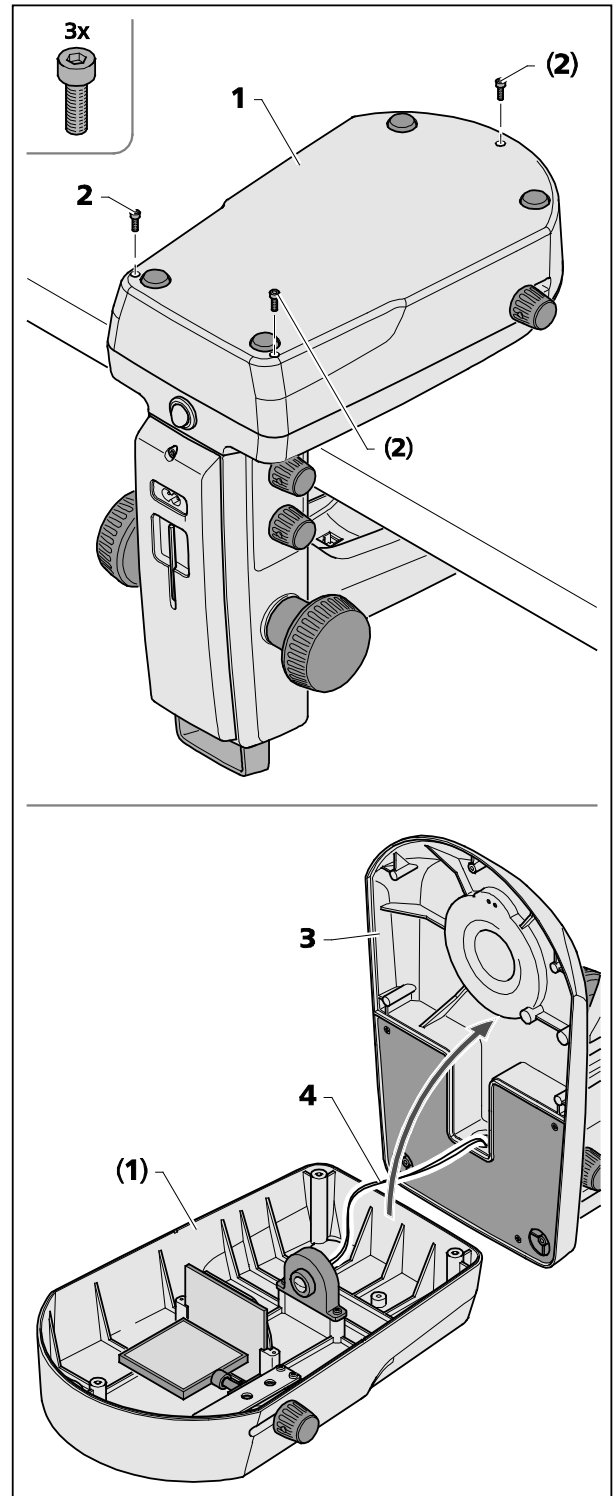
Ouverture de la plaque de fond du statif K LAB
